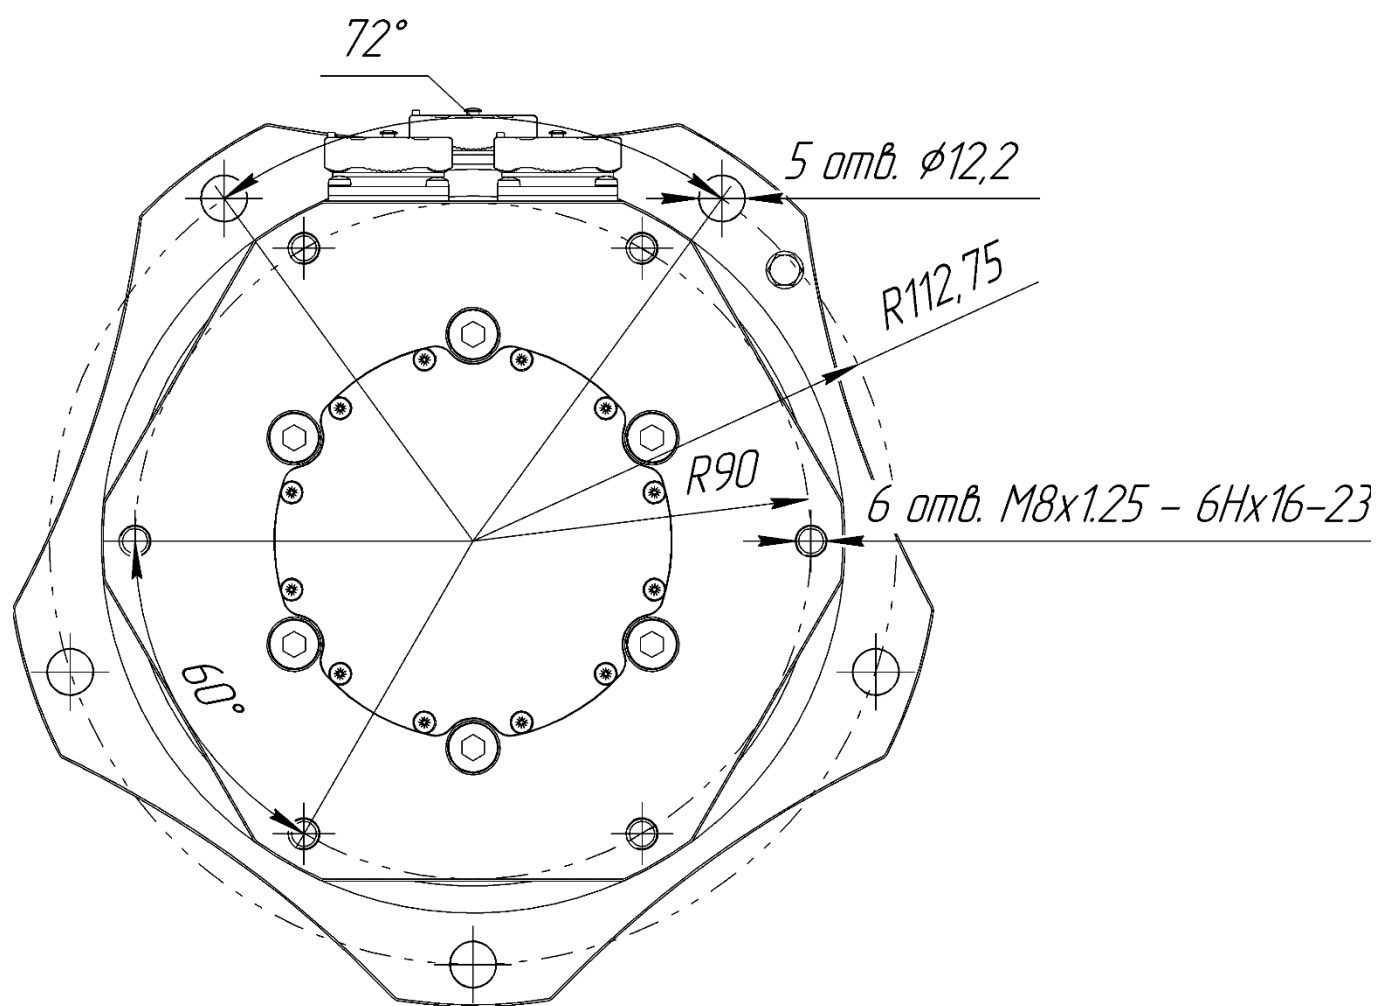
Присоединительные размеры опорно-поворотного устройства (вид сверху)
